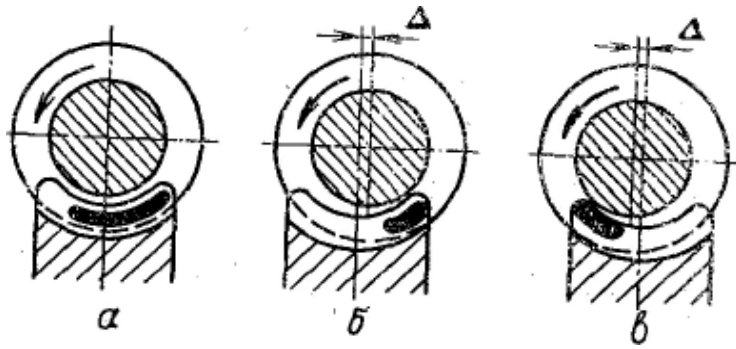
Перевірка установки черв'яка щодо черв'ячного колеса:
